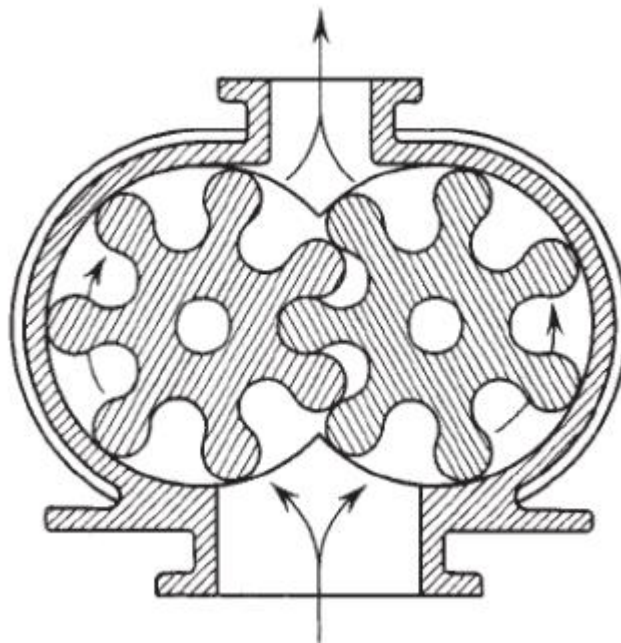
Bomba de deslocamento positivo rotativa de engrenagens.
